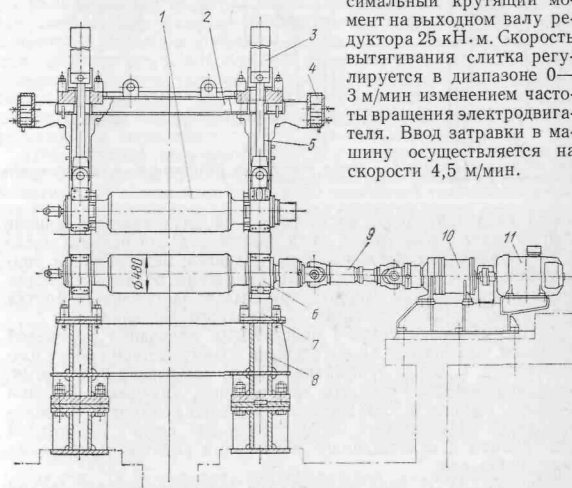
Поперечный разрез тянуще-правильной машины: 1 — верхний неприводный ролик; 2 — поперечные связи; 3 — гидроцилиндры перемещения и прижатия ролика; 4 — продольные балки; 5 — стойки; 6 — нижний ролик; 7 — опорные гидроцилиндры; 8 — станина; 9 — шпиндель с шарнирами Гука; 10 — планетарный редуктор; 11 — электродвигатель
